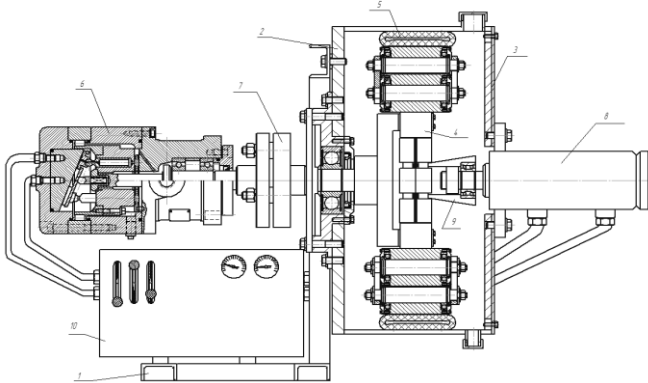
Схема беспоршневого универсального бетононасоса нового конструктивного решения с гидравлическим приводом: 1 – рама; 2 – корпус насоса; 3 – крышка корпуса; 4 – ротор с роликами; 5 – гибкий шланг; 6 – гидромотор; 7 – муфта; 8 – гидроцилиндр; 9 – конический наконечник; 10 – гидрораспределительный узел
